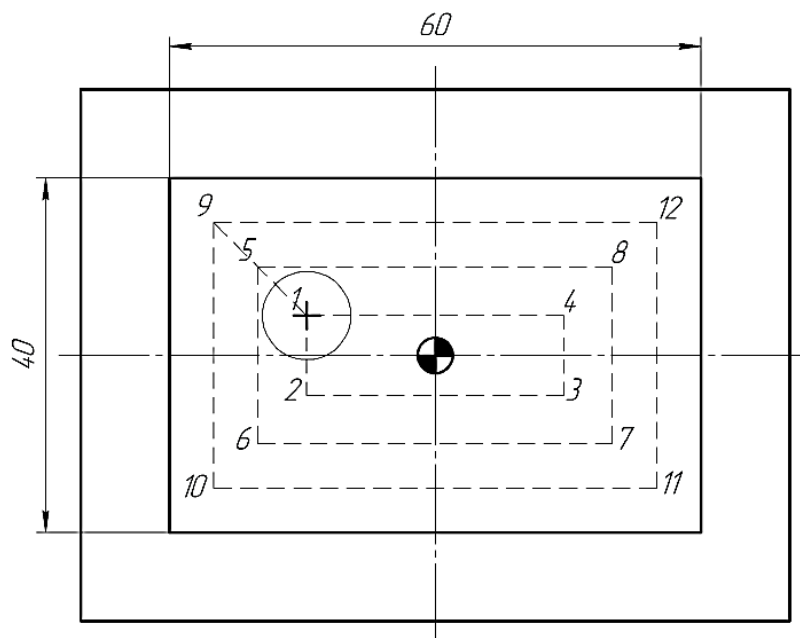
Черновое фрезерование прямоугольного кармана
